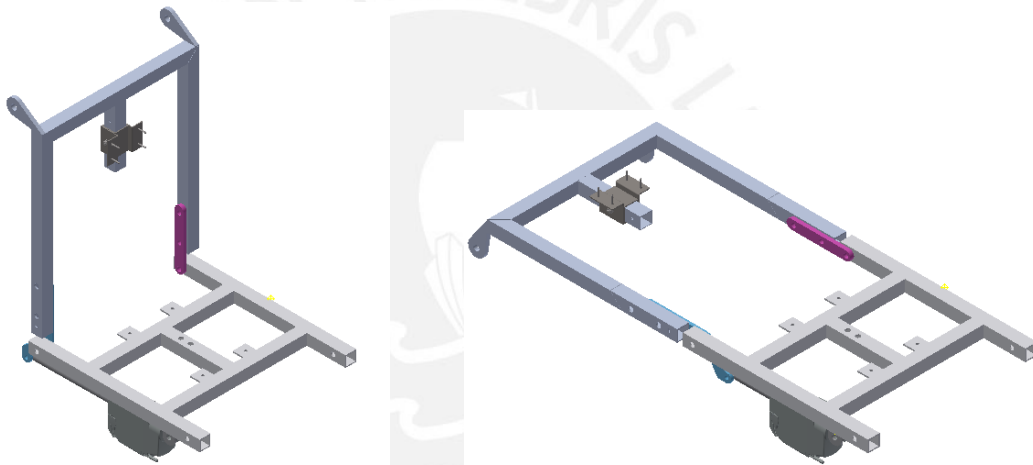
Giro del espaldar - Vistas isométrica de la posición inicial y final
